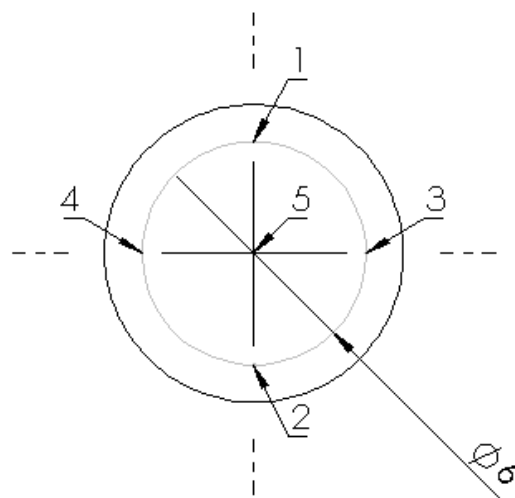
Dimensões do corpo de prova para ensaio SPT.
